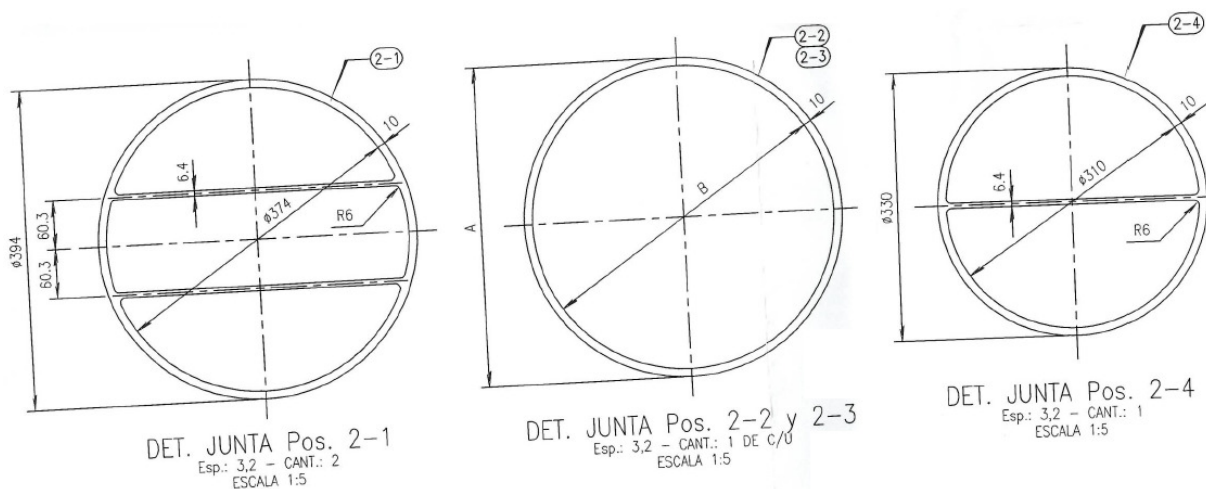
Plano de empaquetaduras enchaquetadas del 3E – 3201 A
